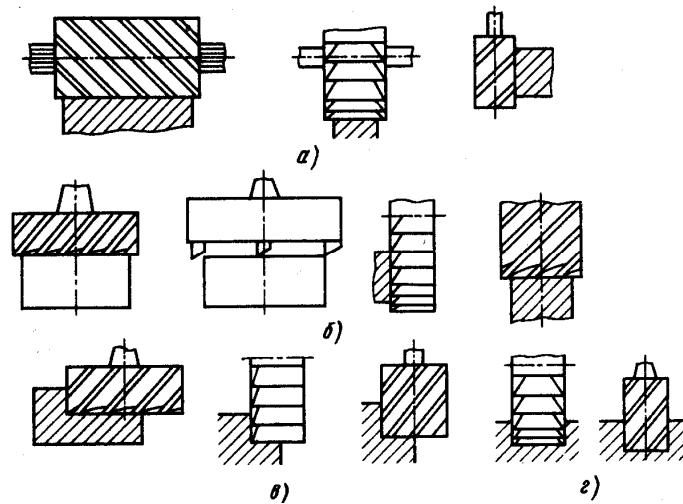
Схемы фрезерования различных плоских поверхностей:
